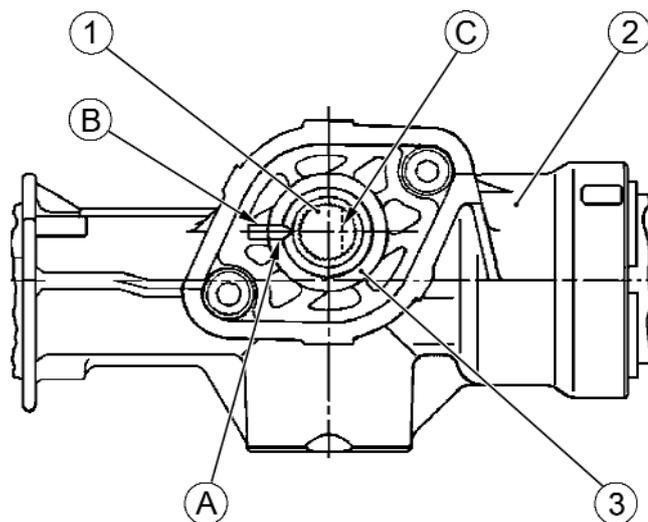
Проверка положения шестерни рулевого механизма:
